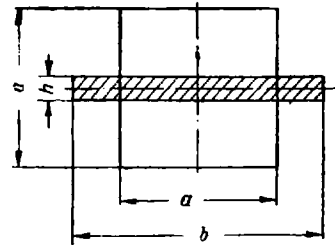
Схема к определению стороны квадратной заготовки при прокатке полосовой стали
